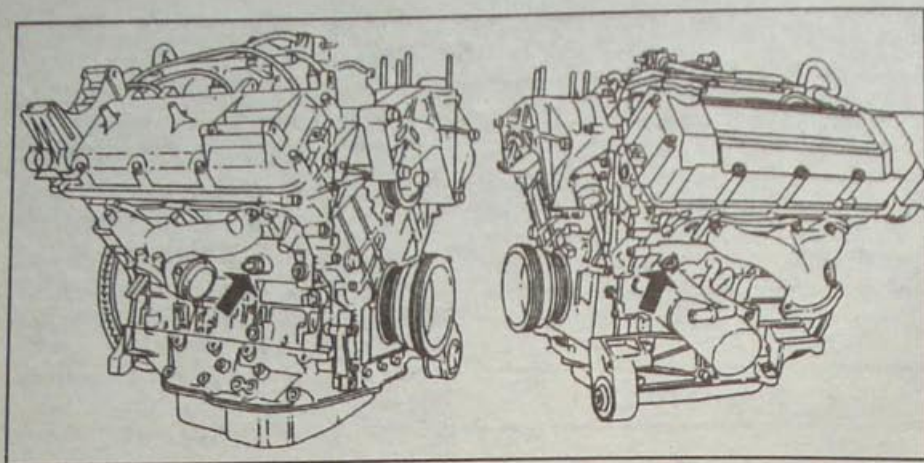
Расположение резьбовых пробок с двух сторон блока цилиндров для слива охлаждающей жидкости
